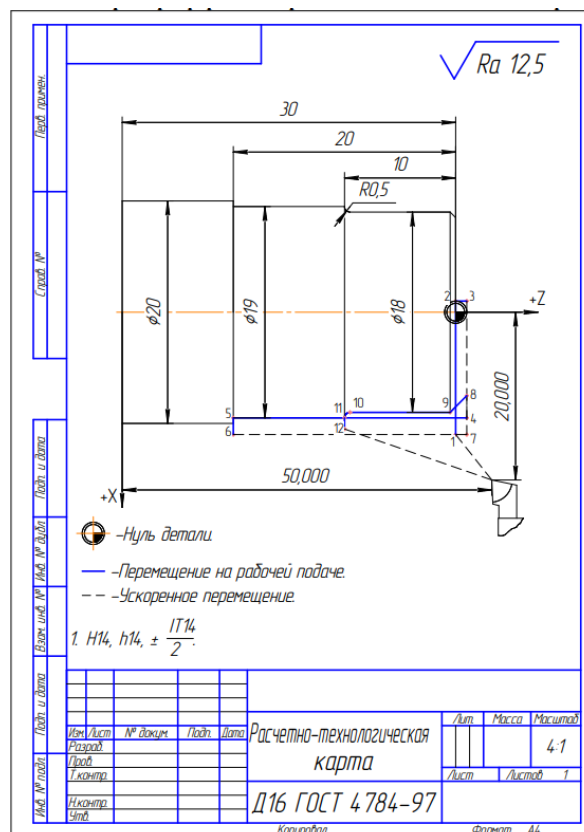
Операционный эскиз, совмещенный с траекторией движения инструмента
